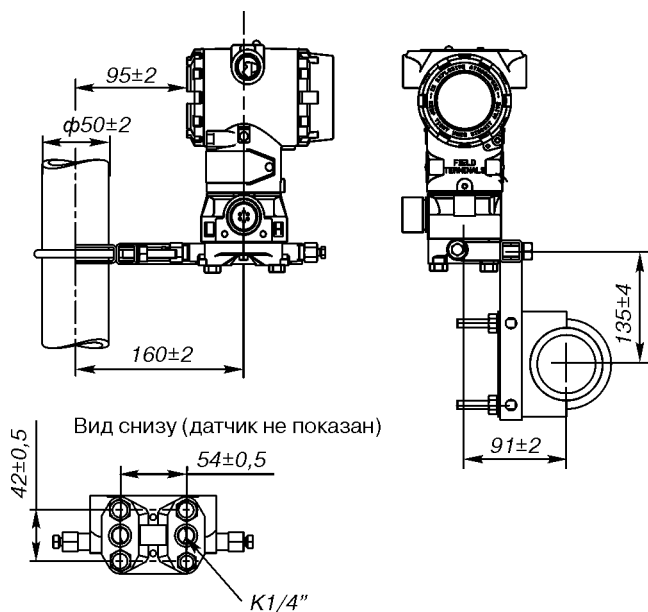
Монтаж на вертикальной или горизонтальной трубе датчиков 3095MV и 3051C расходомеров типа MNF, PNF, MFA.
